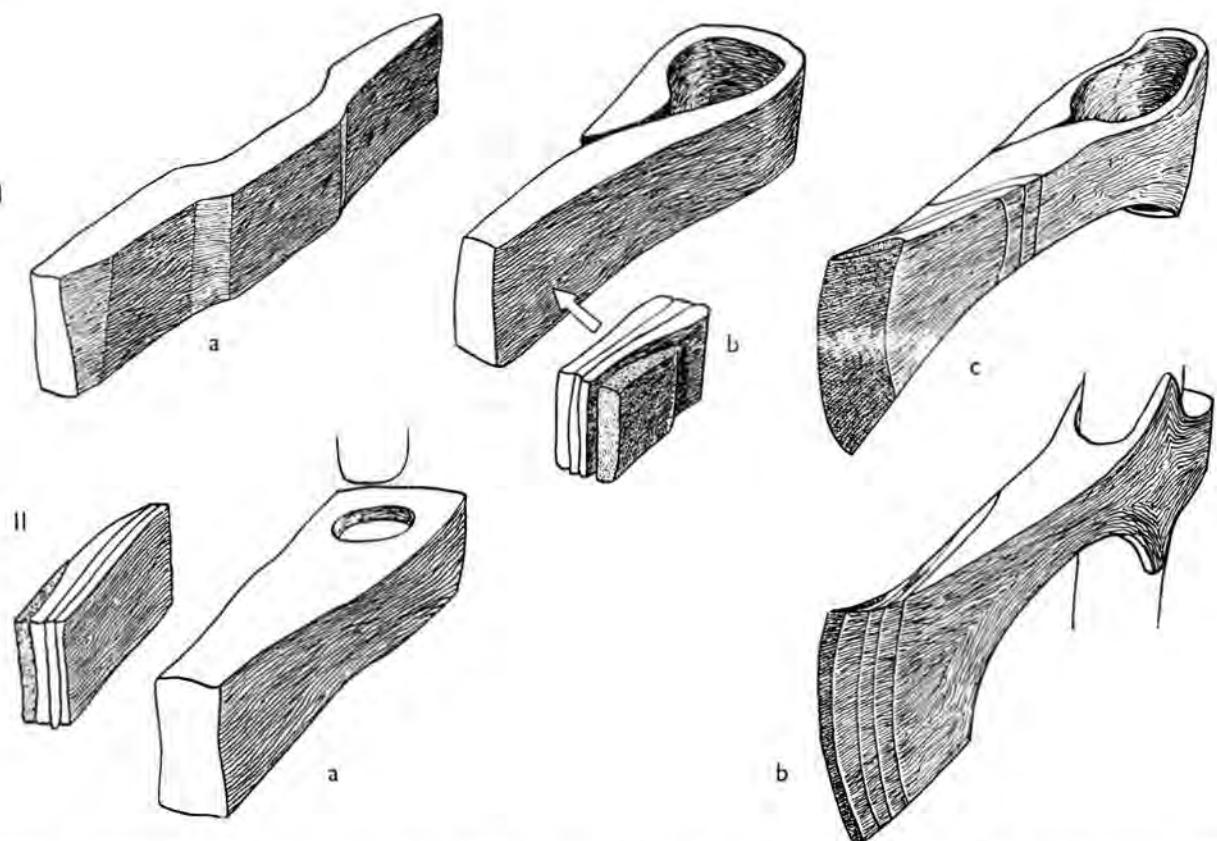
Zwei Herstellungsverfahren der untersuchten Äxte. Obere Reihe (I): Äxte mit umgebogenem und verschweißtem Schaftloch, a — Absetzen des Ausgangsstückes, b — Verschweißen des Schneidestückes (mit einer Stahllamelle) und Verbiegen des Schaftloches, c — Verschweißen des Schaftloches und Fertigstellung des Werkzeugs. Untere Reihe (II): Äxte mit gelochtem Auge, a = Verschweißen des Ausgangsstückes mit dem Schneidenteil (Stahllamelle im Bündel) und Durchlochen des Schaftloches, b = Verformung des Loches und Fertigstellung des Werkzeugs.
